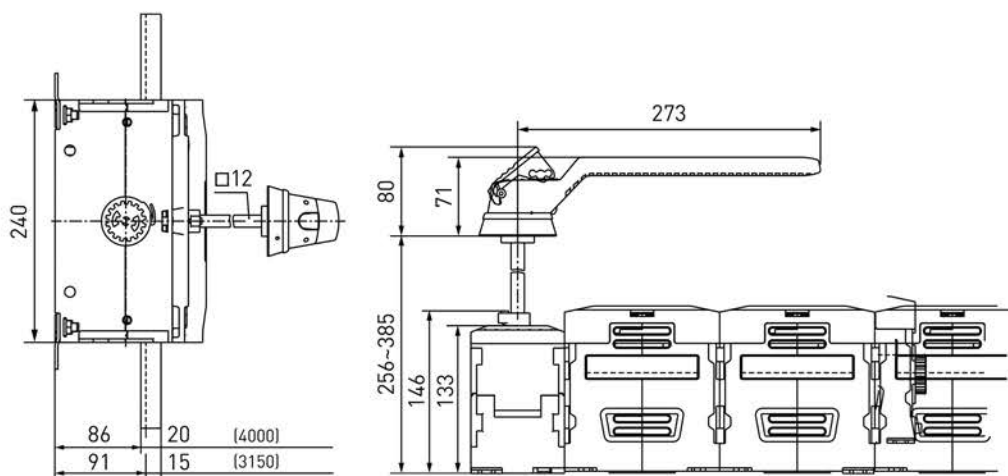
в – Монтажные размеры при установке на дверцу шкафа для рубильников 3150-4000 А
